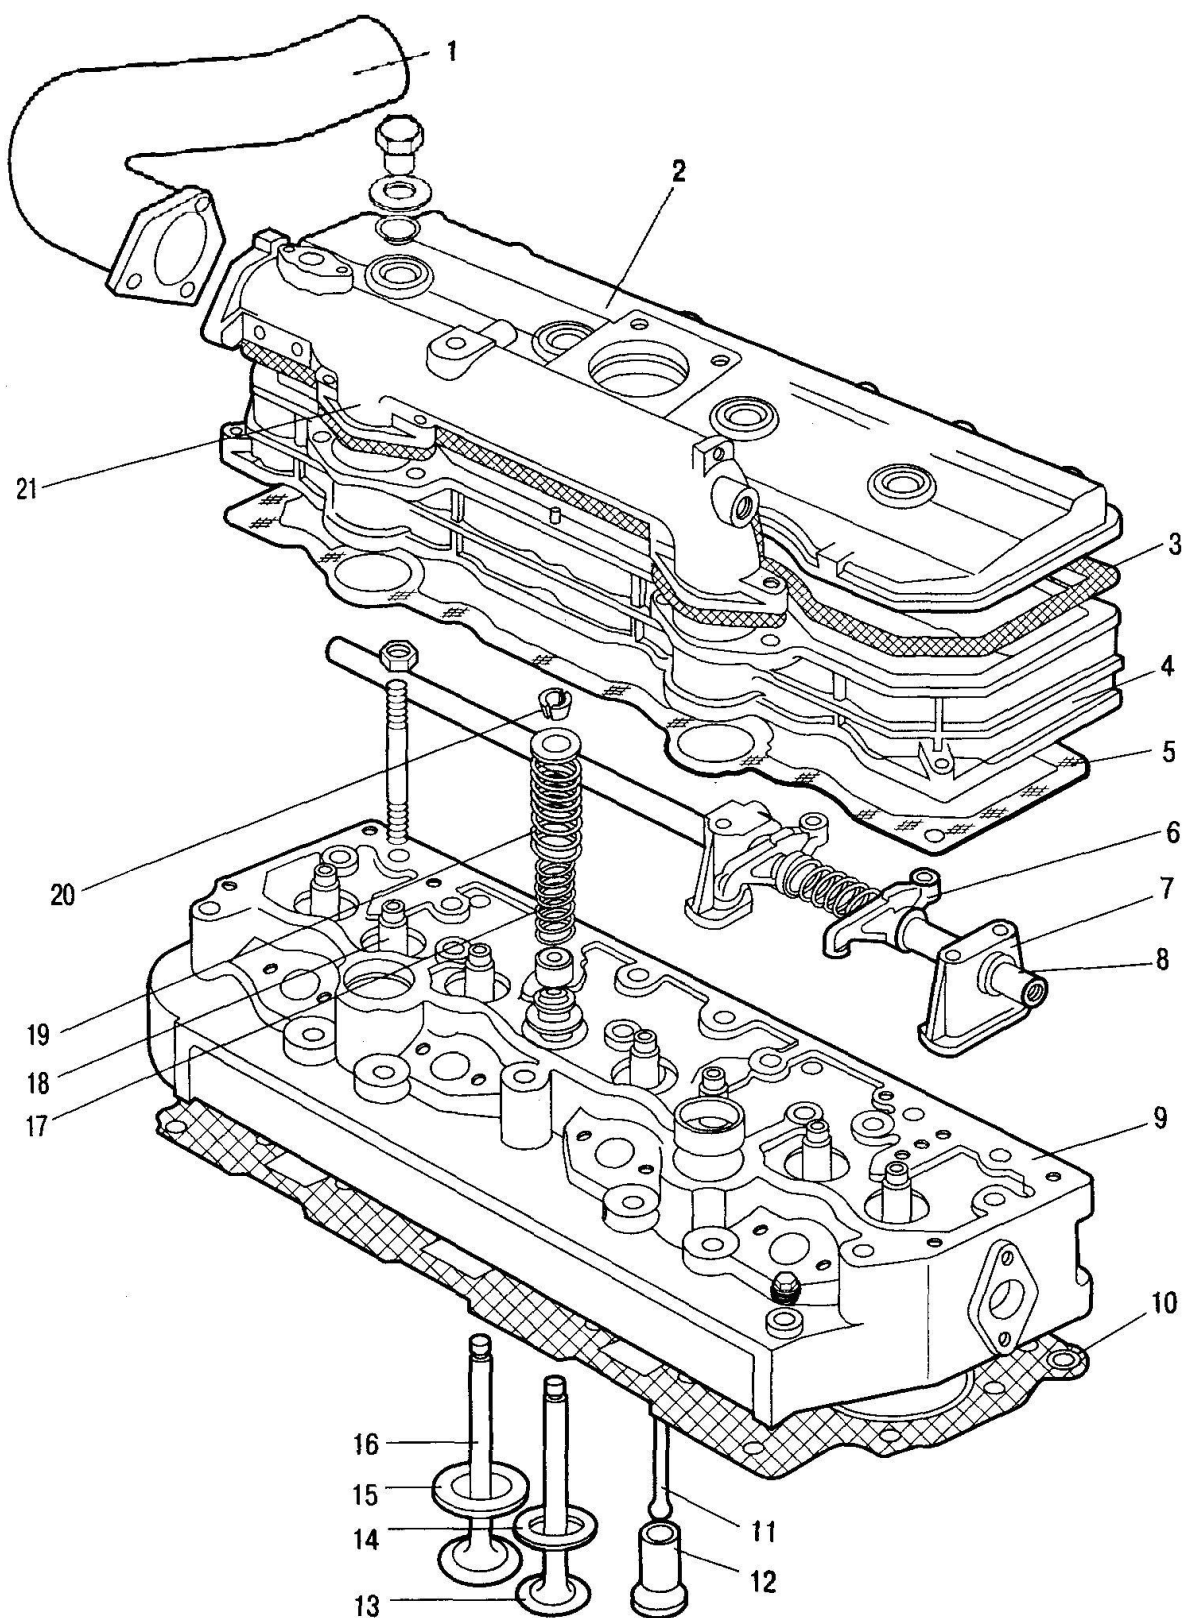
Головка цилиндров и механизм газораспределения:
